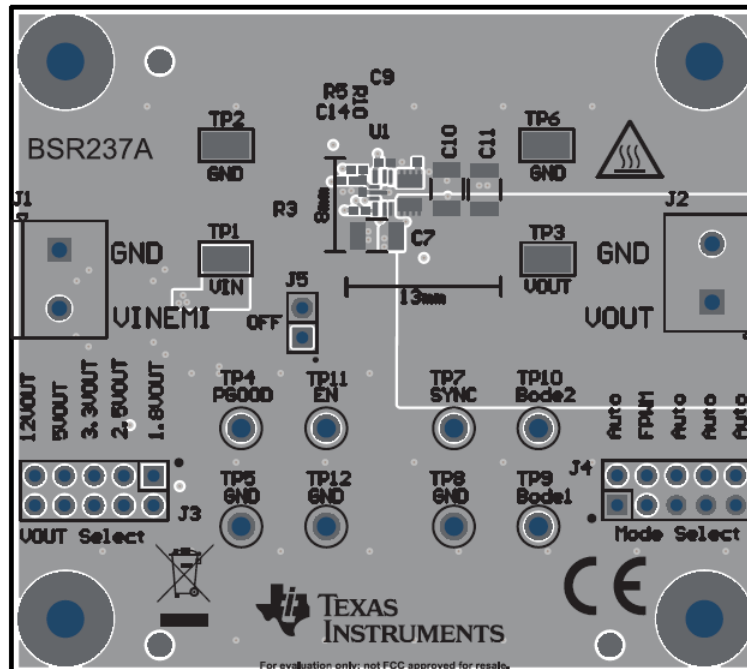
PCB 顶层 2D (TPSM33625FEVM)
